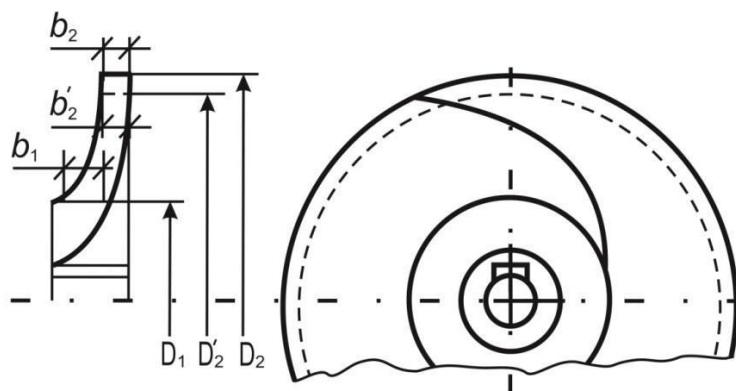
Обрезка рабочего колеса центробежного насоса [10]
